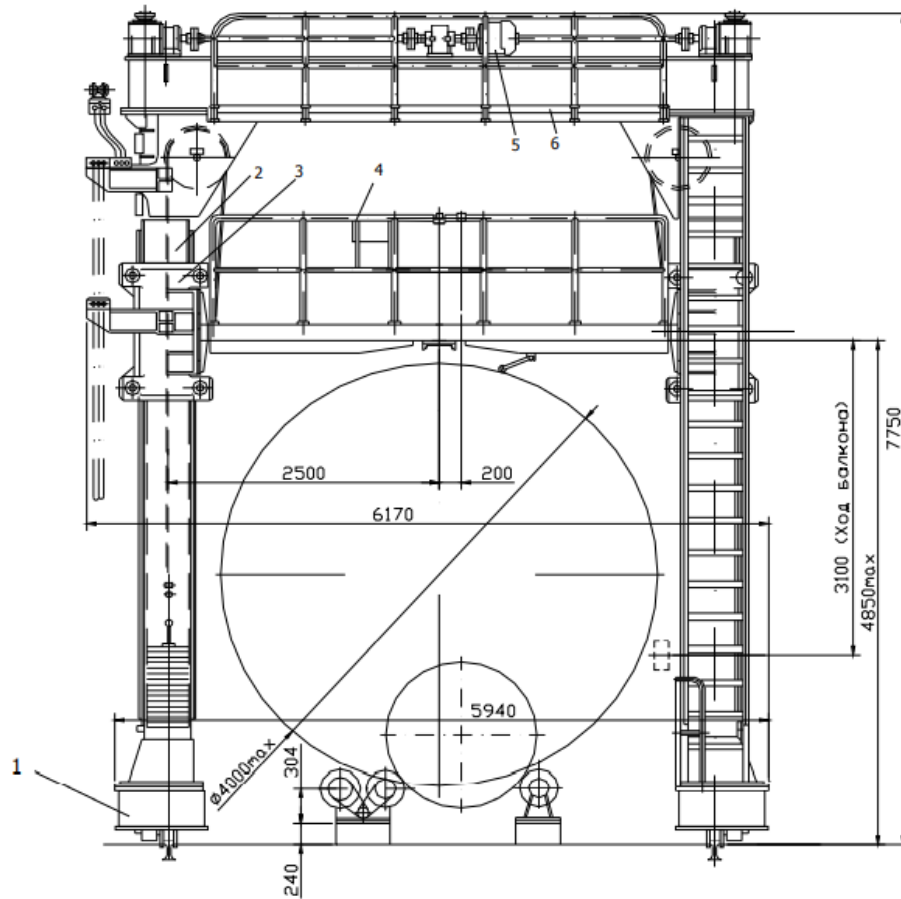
Конструкція порталного візка ПТ-1
